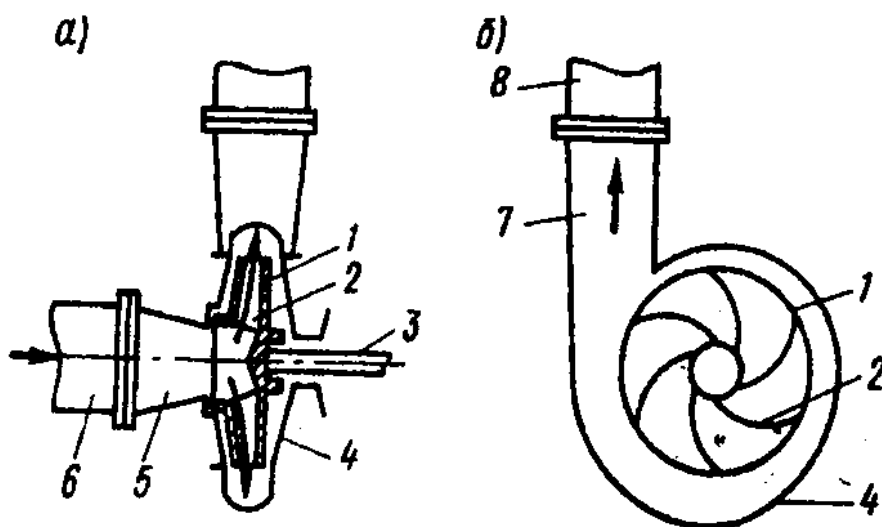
Центробежный насос: а - продольный разрез; б - поперечный; 1 - рабочее колесо; 2 - лопасти рабочего колеса; 3 - вал; 4 - корпус; 5 - всасывающий патрубок; 6 - всасывающий трубопровод; 7 - напорный патрубок; 8 - напорный трубопровод
